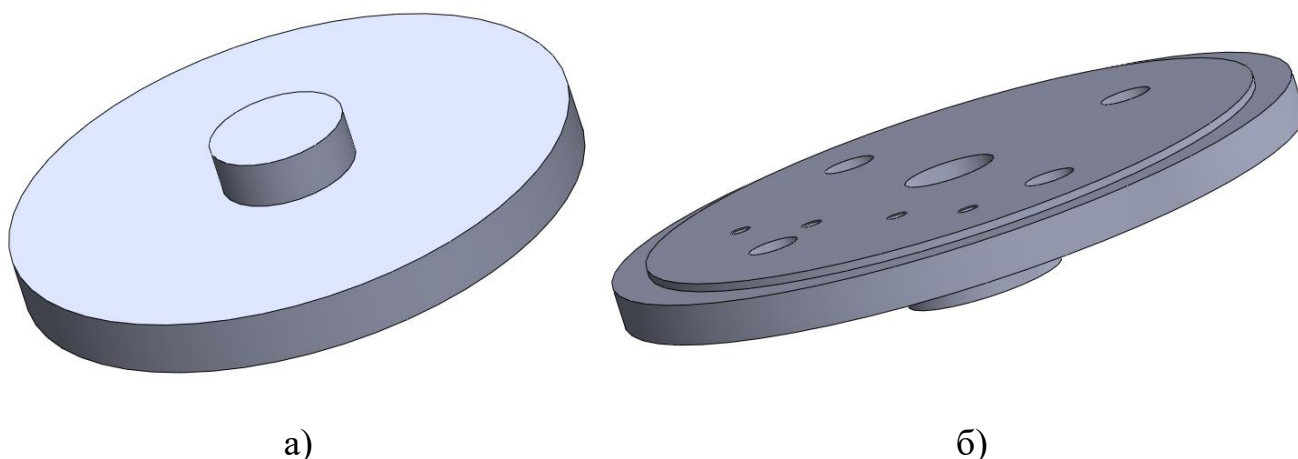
Тривимірні моделі: а – деталь; б – заготовка
